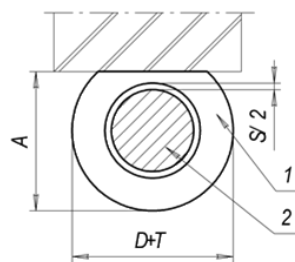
Установка заготовки на цилиндрический палец
